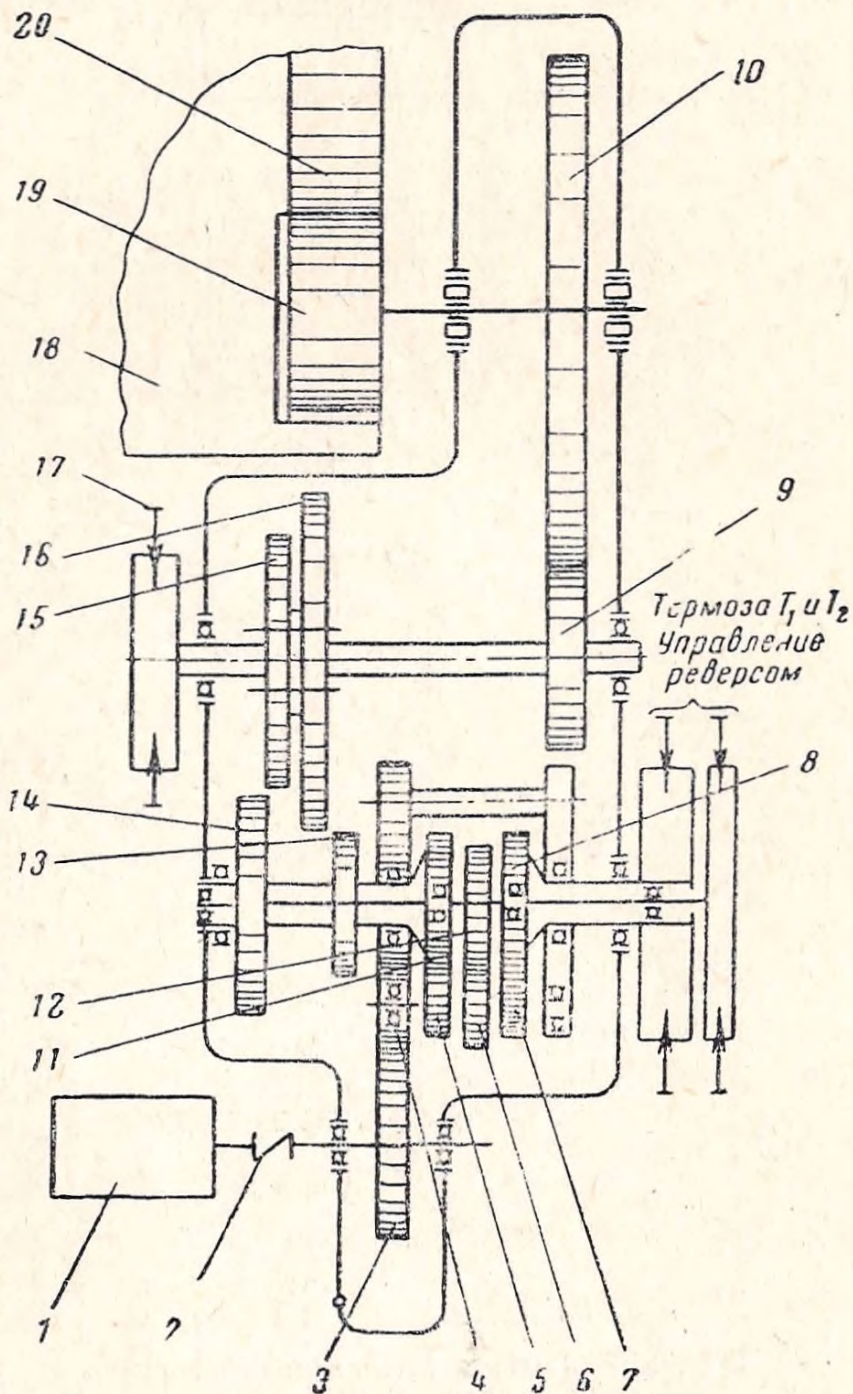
Кинематическая схема моторного катка Д-400А:
